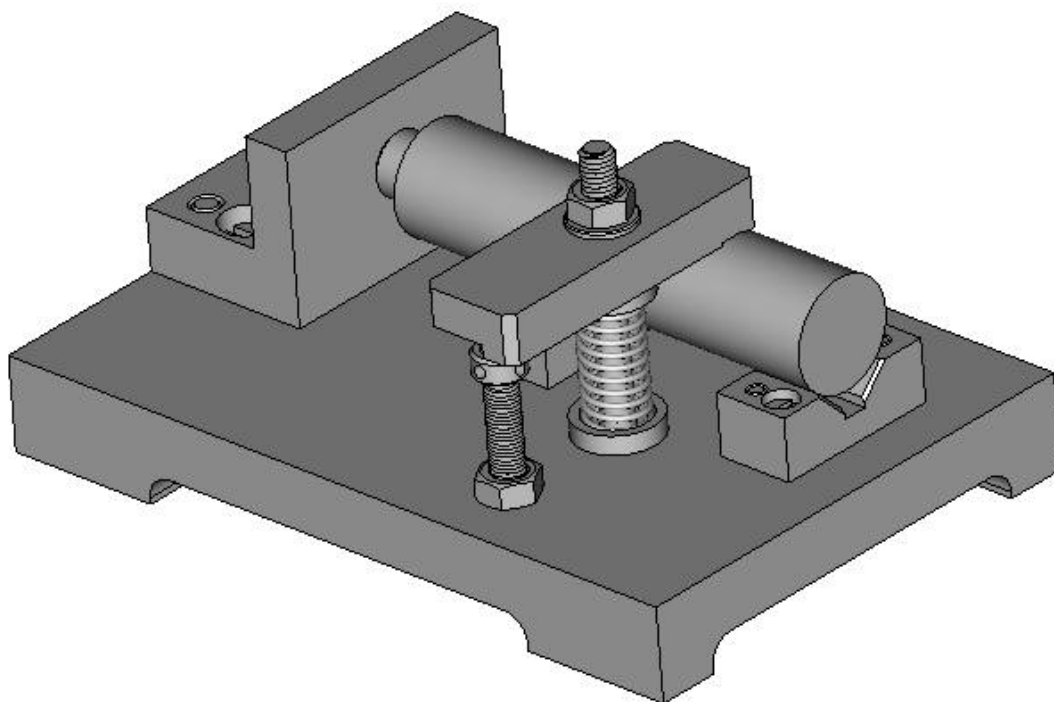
Зажимное приспособление для цилиндра на призмах
